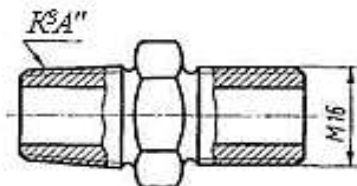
Пример конической (слева) и цилиндрической (справа) резьбы
